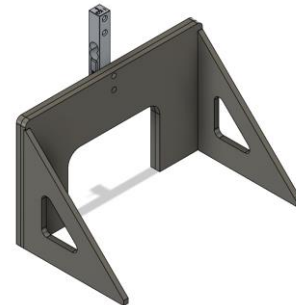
Isométrico de soporte de celda de carga ensamblado
